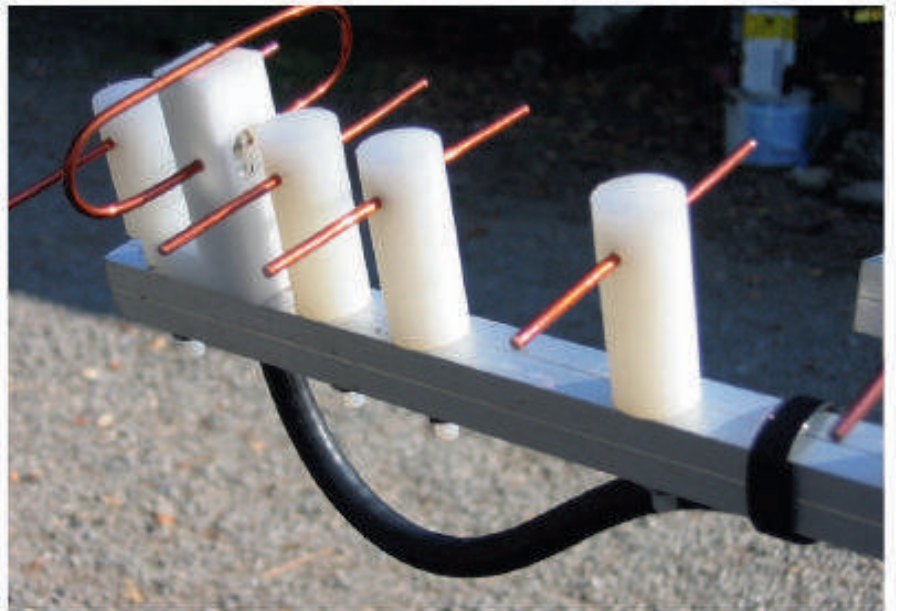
DETAIL MONTAGE TROMBONE ET ATTAQUE DU COAXIAL
